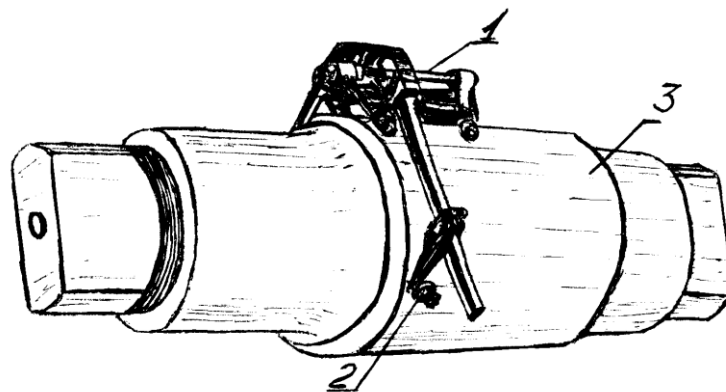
Пасометр: 1 – візок; 2 – індикатор; 3 – бочка валка
